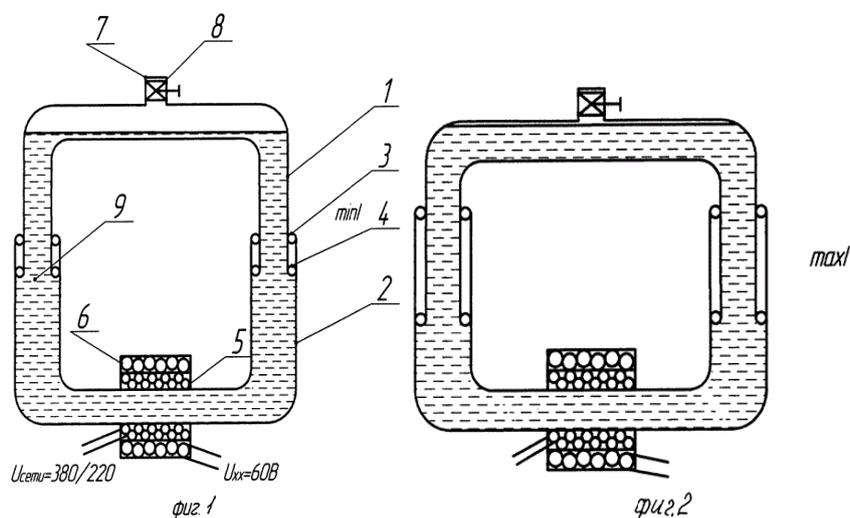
Схема источника питания сварочной дуги (обозначения в тексте)
